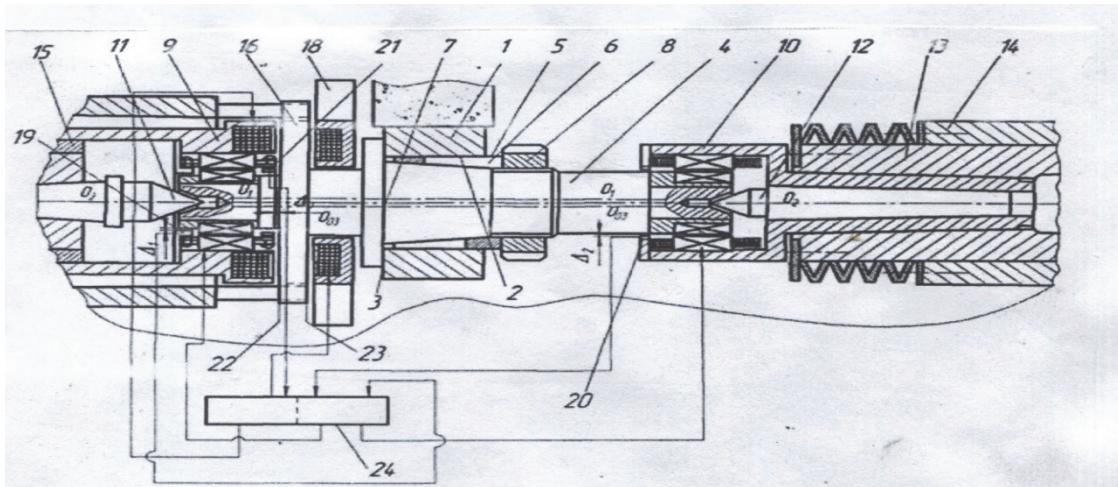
Схема установки заготовки с оправкой с базированием по их оси на центры с переходом на электромагнитные опоры (патент 2237565)
